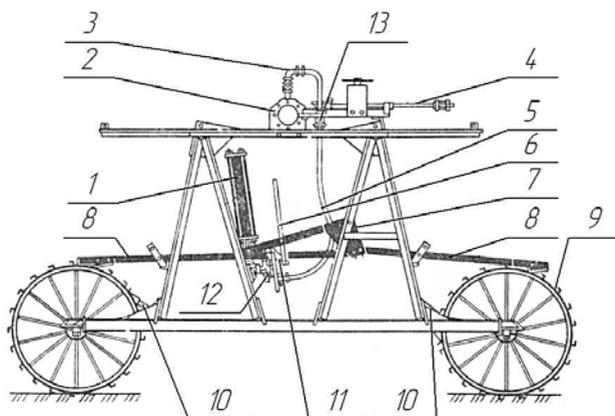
Гидропривод тележки машины «Фрегат»: 1 – гидроцилиндр; 2 – трубопровод водопроводящий; 3 – подводящая труба; 4 – стержень; 5 – напорный рукав; 6 – тяга; 7 – двуплечий рычаг; 8 – толкающие штанги; 9 – колесо тележки; 10 – стопор; 11 – рычаг-переключатель; 12 – клапан-распределитель; 13 – дроссельный клапан
